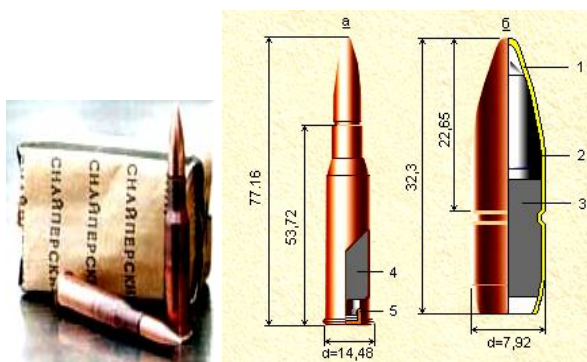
7,62 мм винтовочный снайперский патрон (7Н1) с бронебойной пулей, а – патрон, б – пуля: 1 – оболочка; 2 – сердечник стальной; 3 – сердечник свинцовый; 4 – метательный заряд; 5 – капсюль-воспламенитель
